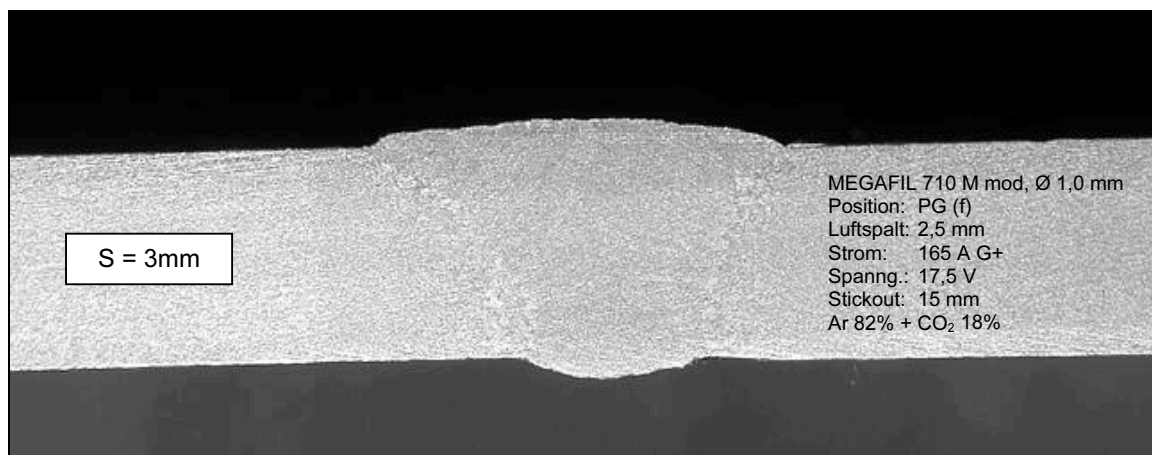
Makroschliff einer in PG-Position ausgeführten Einlagenschweißung
